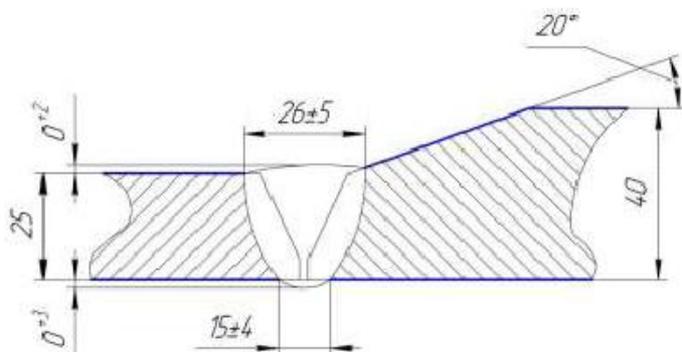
Конструктивные размеры сварного шва
